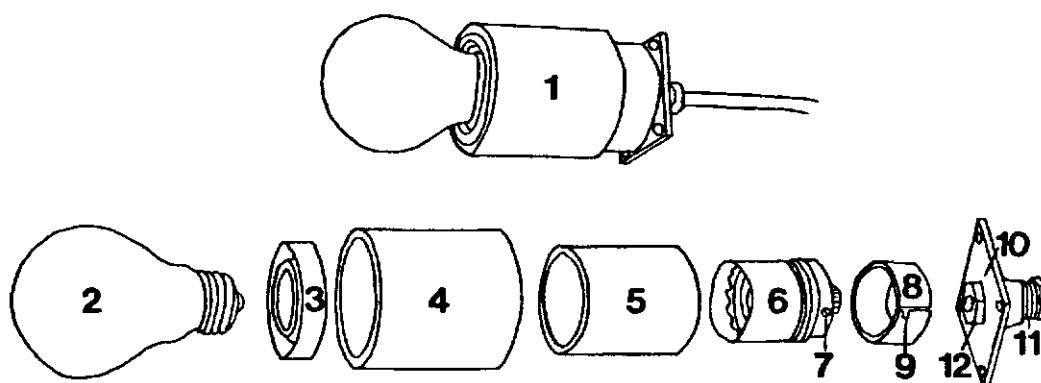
Montagezeichnung für ein wasserdichtes Lampenfassungsgehäuse
